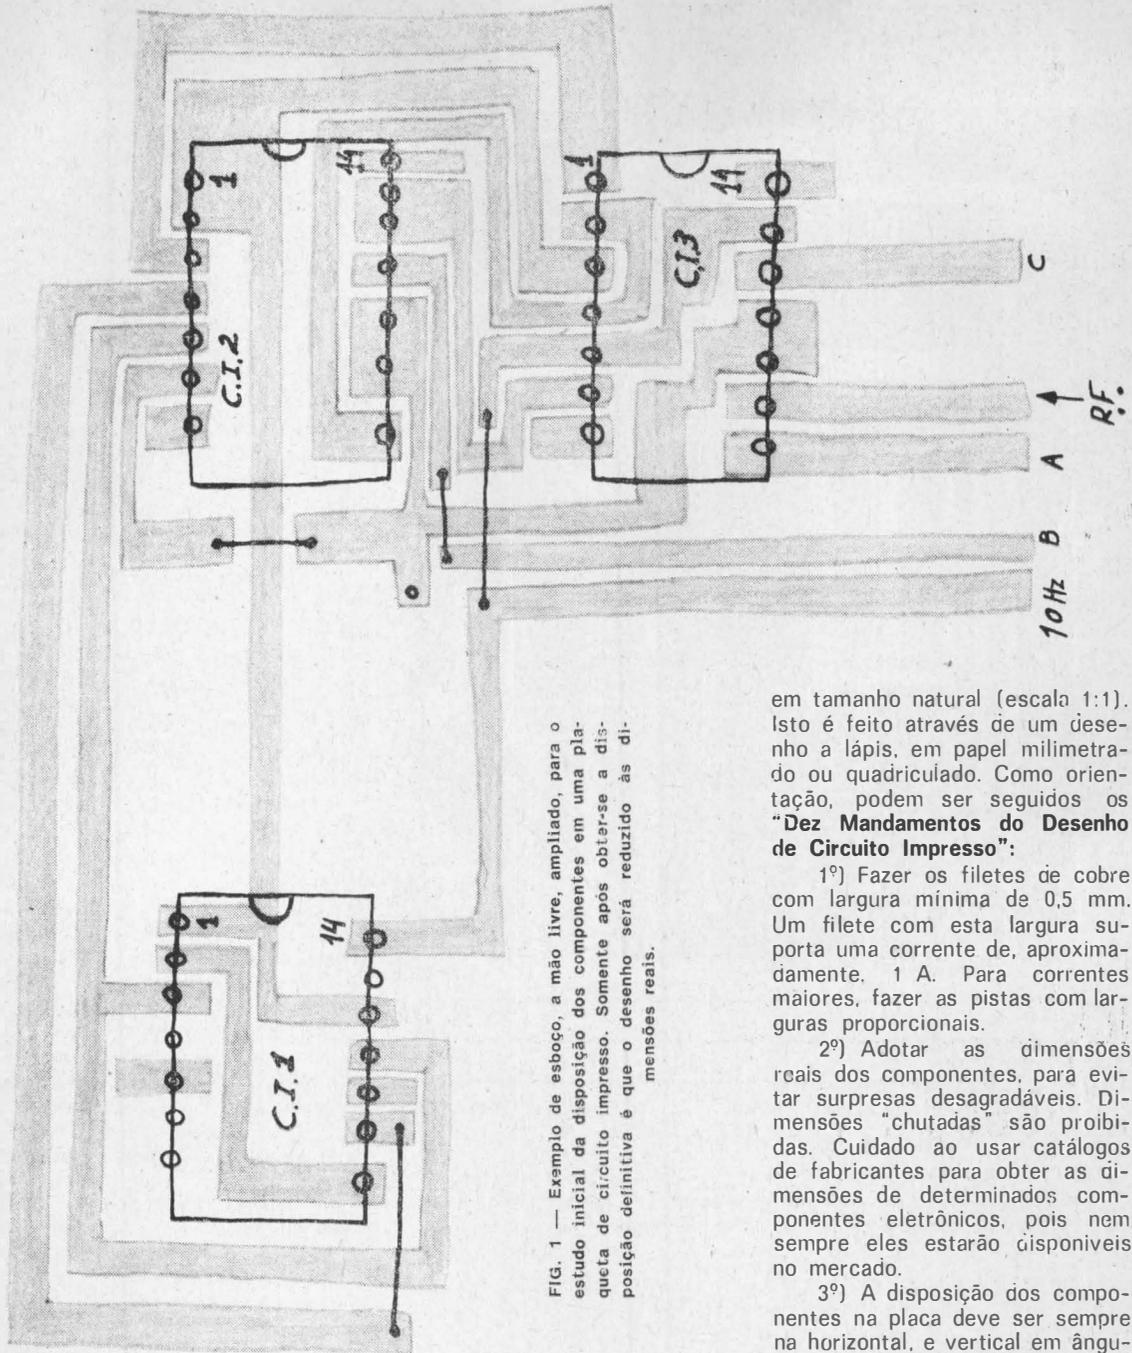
Exemplo de esboço, a mão livre, ampliado, para o estudo inicial da disposição dos componentes em uma placa de circuito impresso. Somente após obter-se a disposição definitiva é que o desenho será reduzido às dimensões reais.
